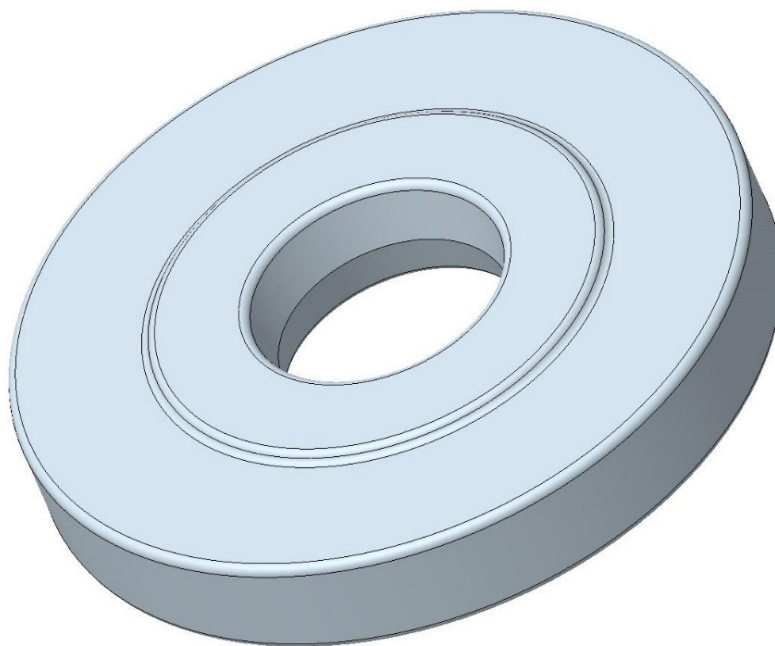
Трехмерная модель отливки «фланец» из стали 20Л
